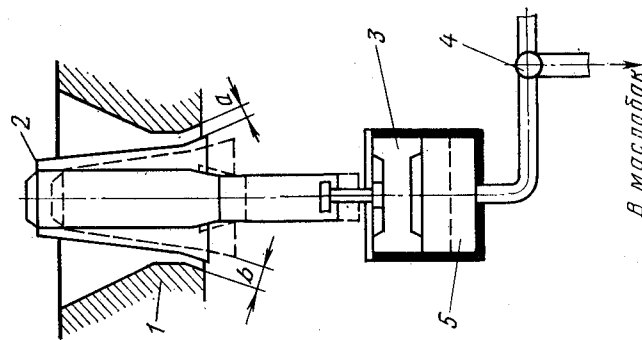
Гидравлическое устройство для регулирования разгрузочной щели дробилки ККД-1500/180
